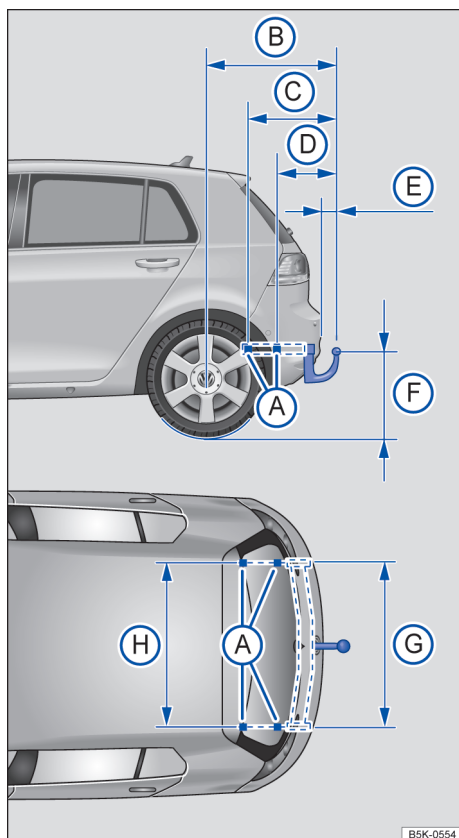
Dimensões e pontos de fixação para instalar um dispositivo de reboque posteriormente.
